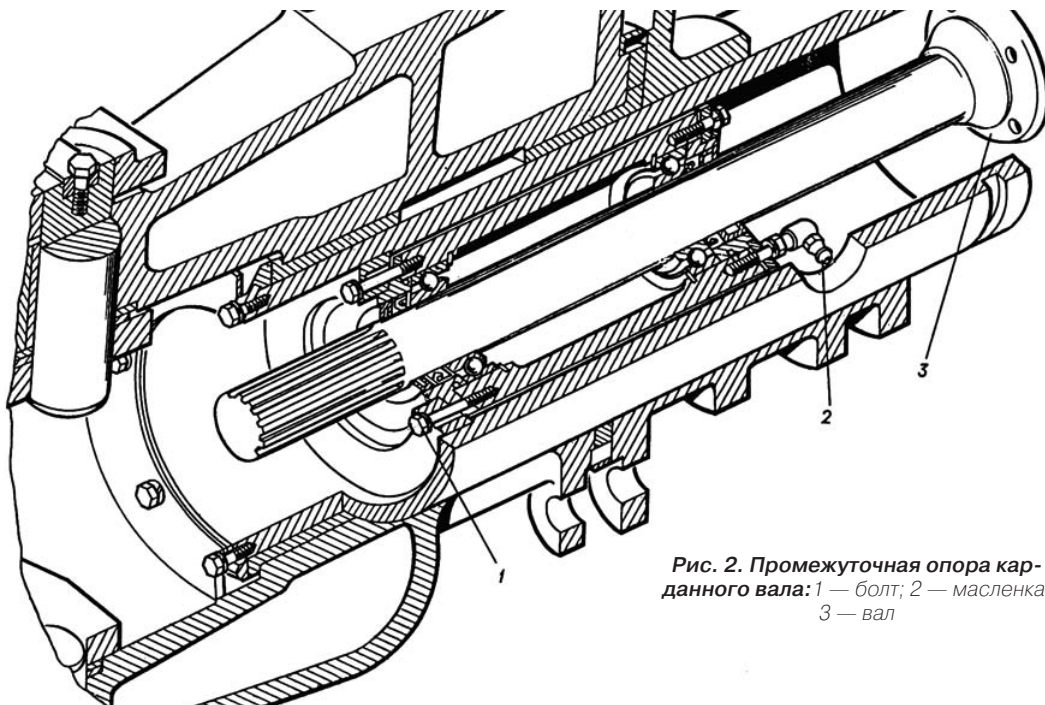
Промежуточная опора карданного вала: 1 — болт; 2 — масленка; 3 — вал
